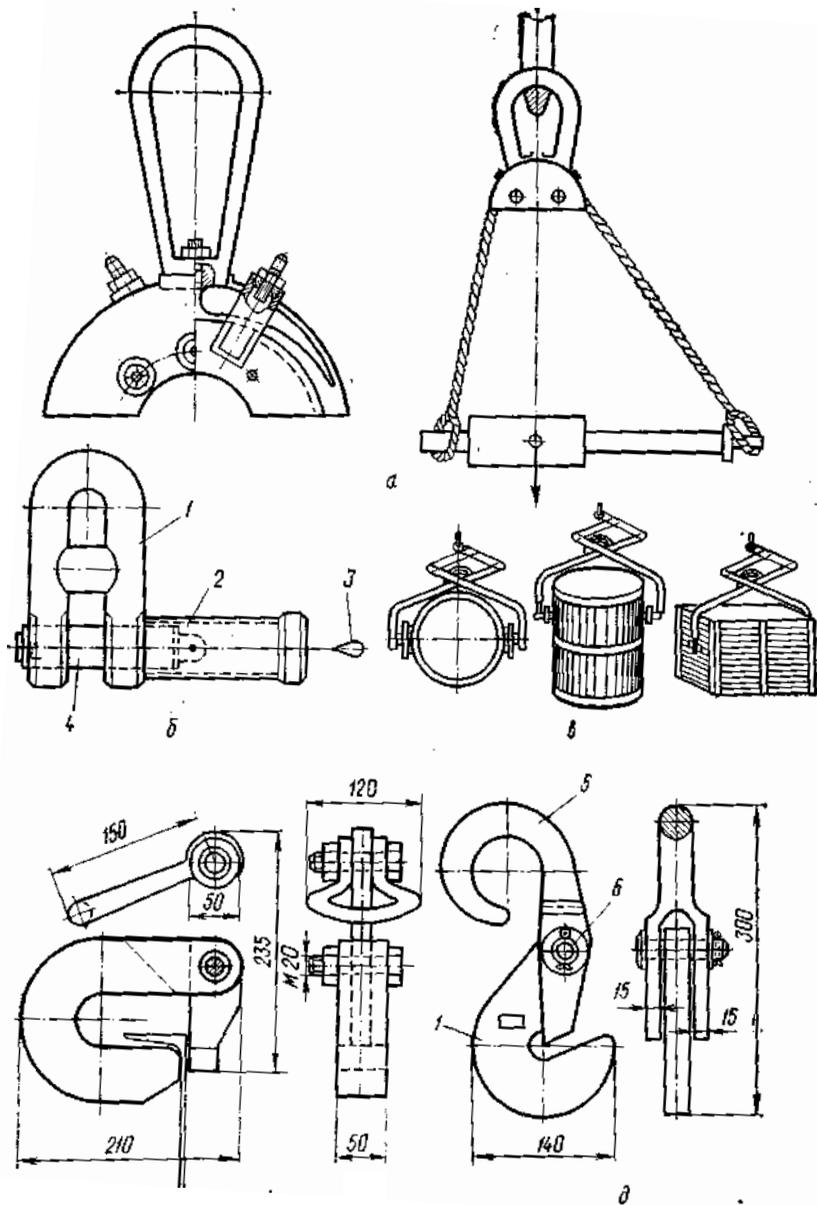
Приспособления для захвата оборудования и элементов металлоконструкций и металлопроката:
